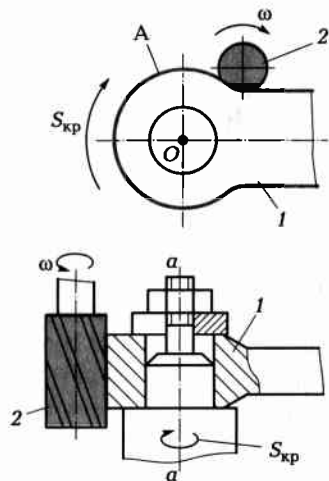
Схема обработки незамкнутой цилиндрической поверхности
